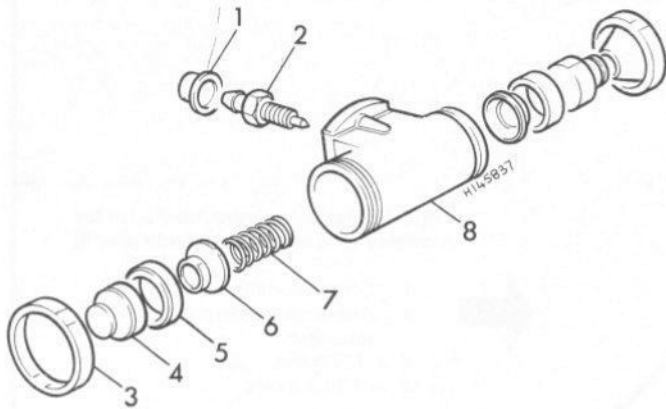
Eclaté d'un cylindre de roue arrière (Sec 7)
